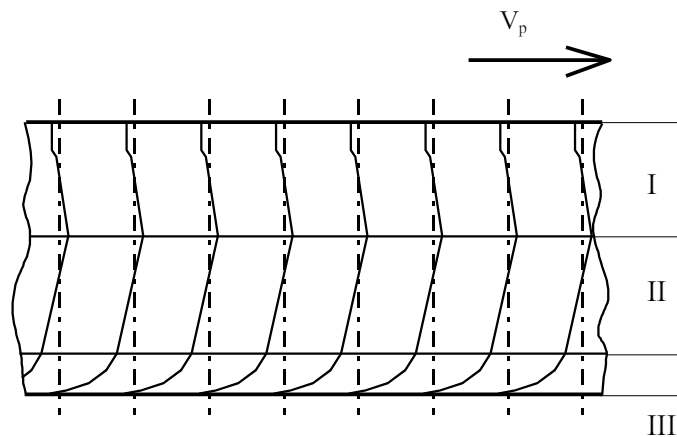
Схема розташування борозен на поверхні різну вуглецевій сталі
